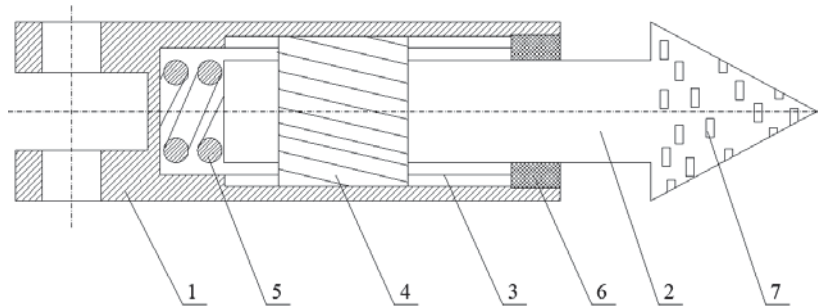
Зуб ковшу землерийної машини: 1 – корпус-адаптер; 2 – коронка; 3 – гвинтові нарізи у корпусі; 4 – виступи на тілі коронки; 5 – гвинтова пружина; 6 – ущільнювальний елемент; 7 – вставки з карбіду вольфраму
